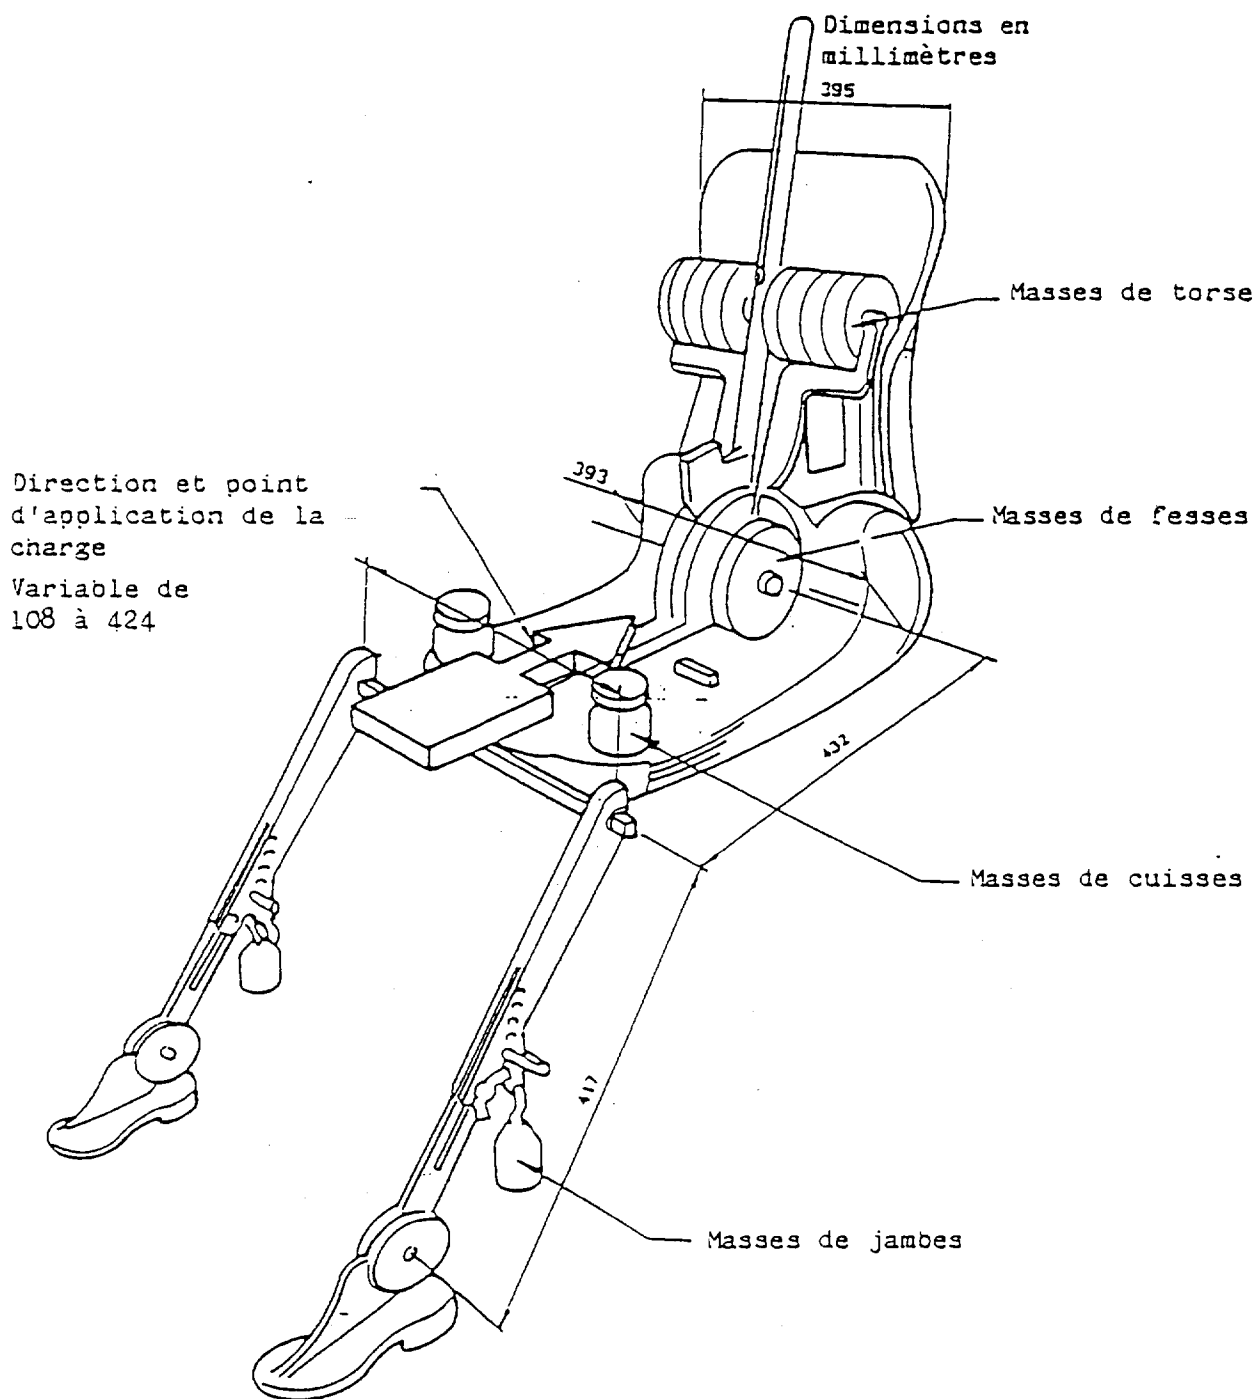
Dimensions des éléments de la machine 3-D H et emplacement des masses
